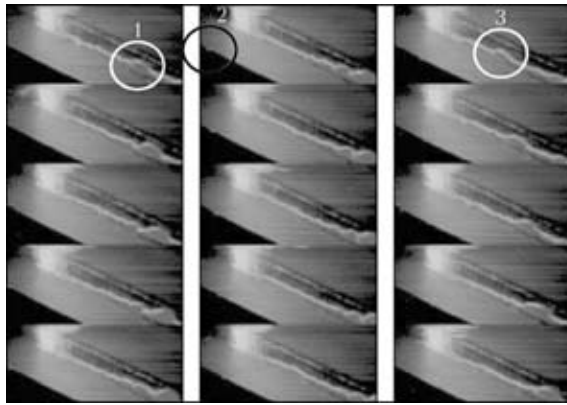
Динамика роста бугров сварочной ванны (видео съемка в процессе сварки)
